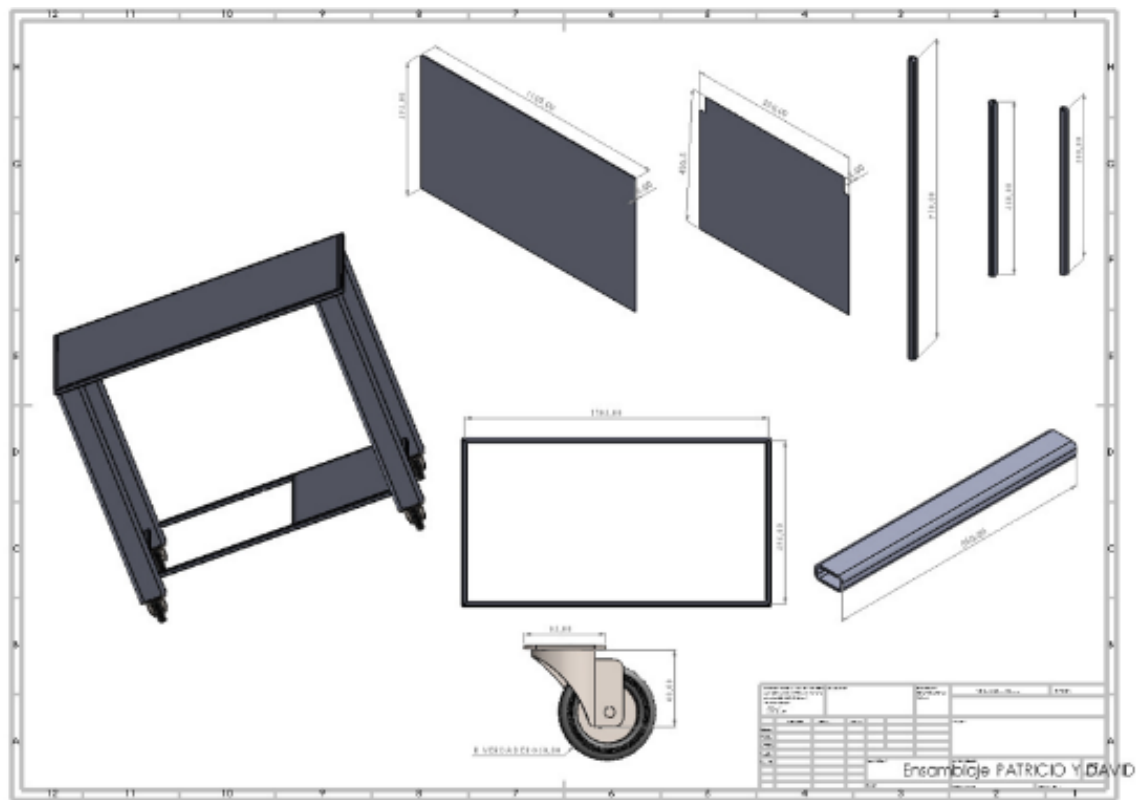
Medidas para mesa soldadura TIG
